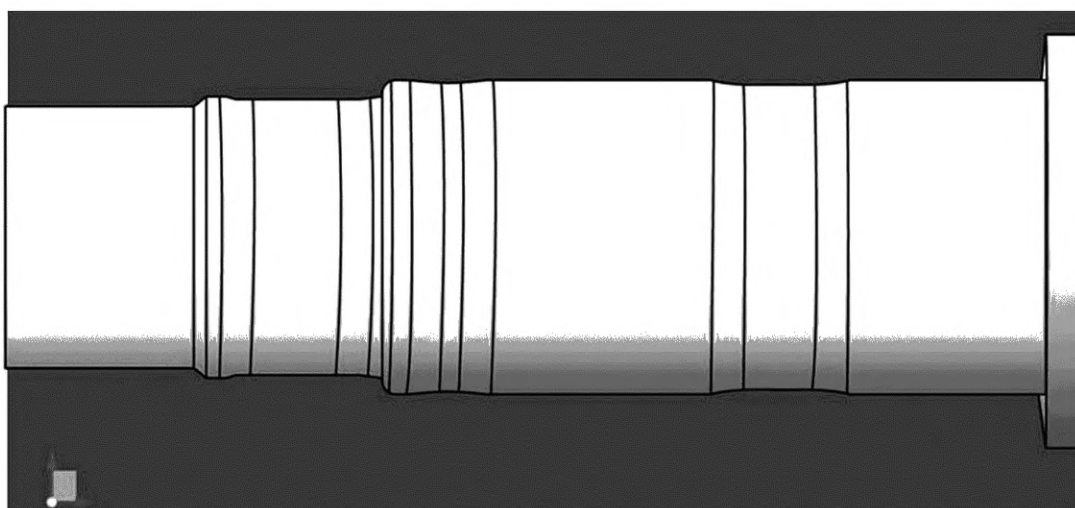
CAD-изображение нескольких областей вала после предлагаемой механической обработки для подготовки поверхности к восстановлению
